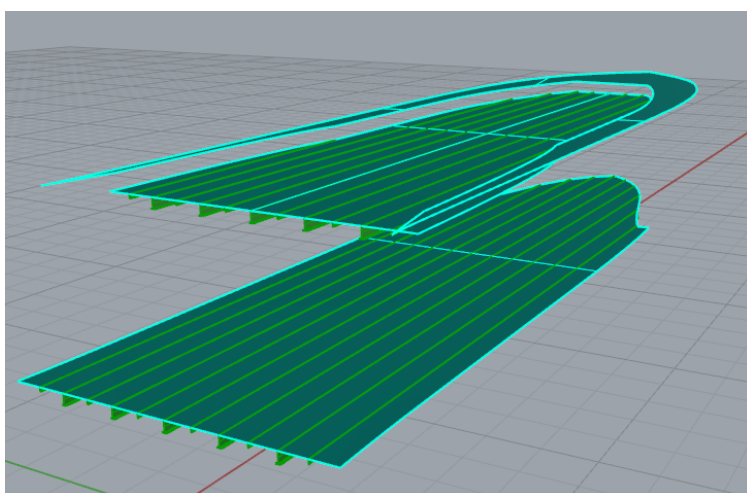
Disposición de los refuerzos longitudinales de las cubiertas.
